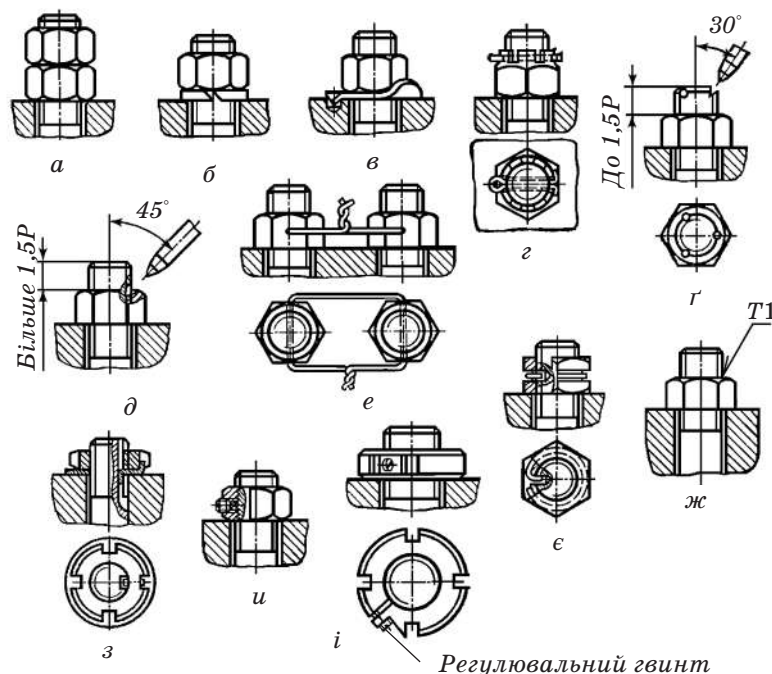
Способи стопоріння різьбових з'єднань:
